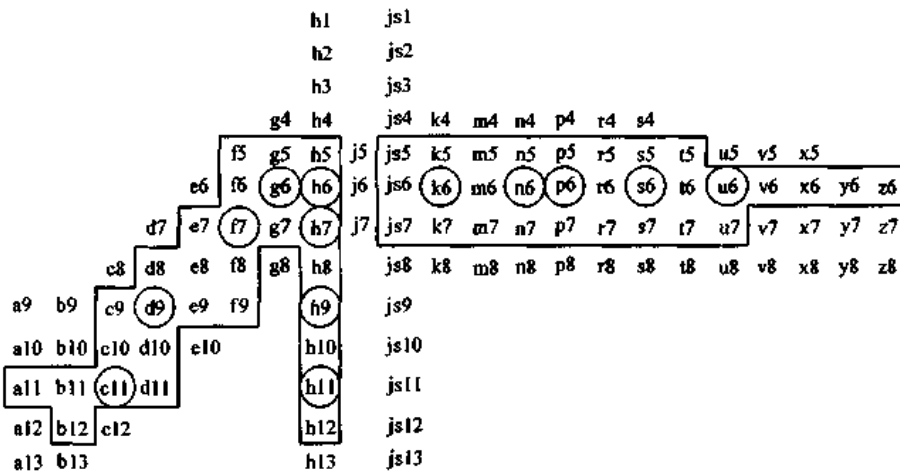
基本尺寸至 500mm 的轴公差带
